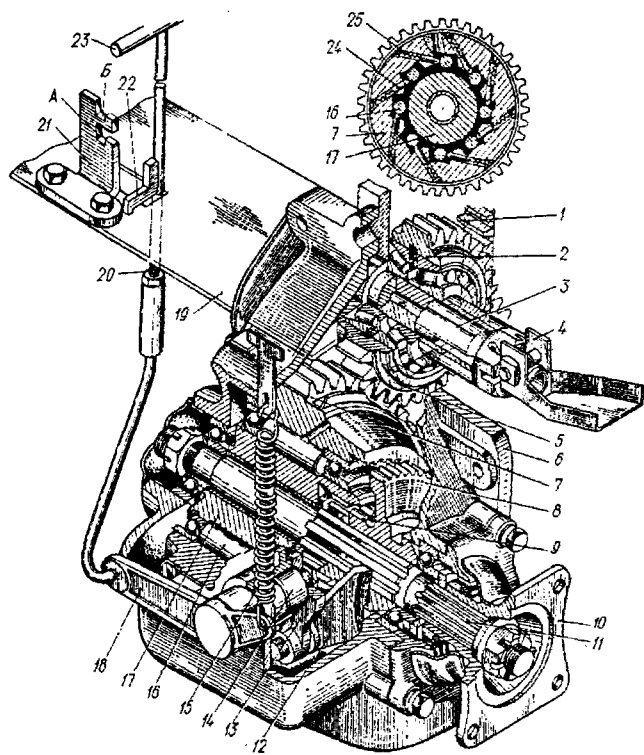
Раздаточная коробка полноприводных тракторов МТЗ и ЮМЗ: 1 – шестерня вторичного вала коробки передач; 2 – промежуточная шестерня; 3 – ось; 4 – лоток; 5 – болт; 6 – корпус; 7 – шестерня наружной обоймы муфты свободного хода; 8, 9 – зубчатые муфты; 10 – фланец; 11 – вал; 12 – вилка; 13, 14 – рычаги управления; 15 – пружина; 16 – ролик муфты свободного хода; 17 – внутренняя обойма муфты свободного хода; 18 – рычаг управления; 19 – пол кабины; 20 – тяга; 21 – стойка; 22 – упор; 23 – рукоятка; 24 – штифт; 25 – пружина обгонной муфты
